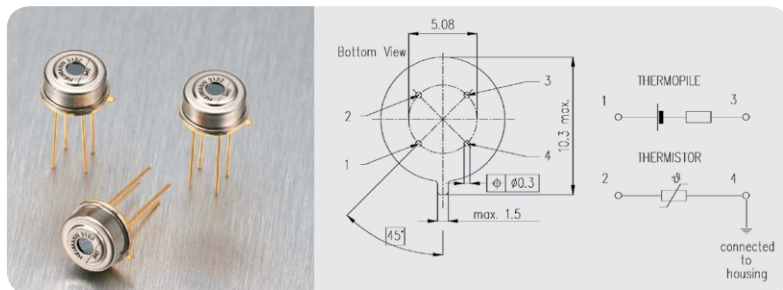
Der Thermopile-Sensor TPS 334 mit Anschlussbelegung und Innenschaltung
